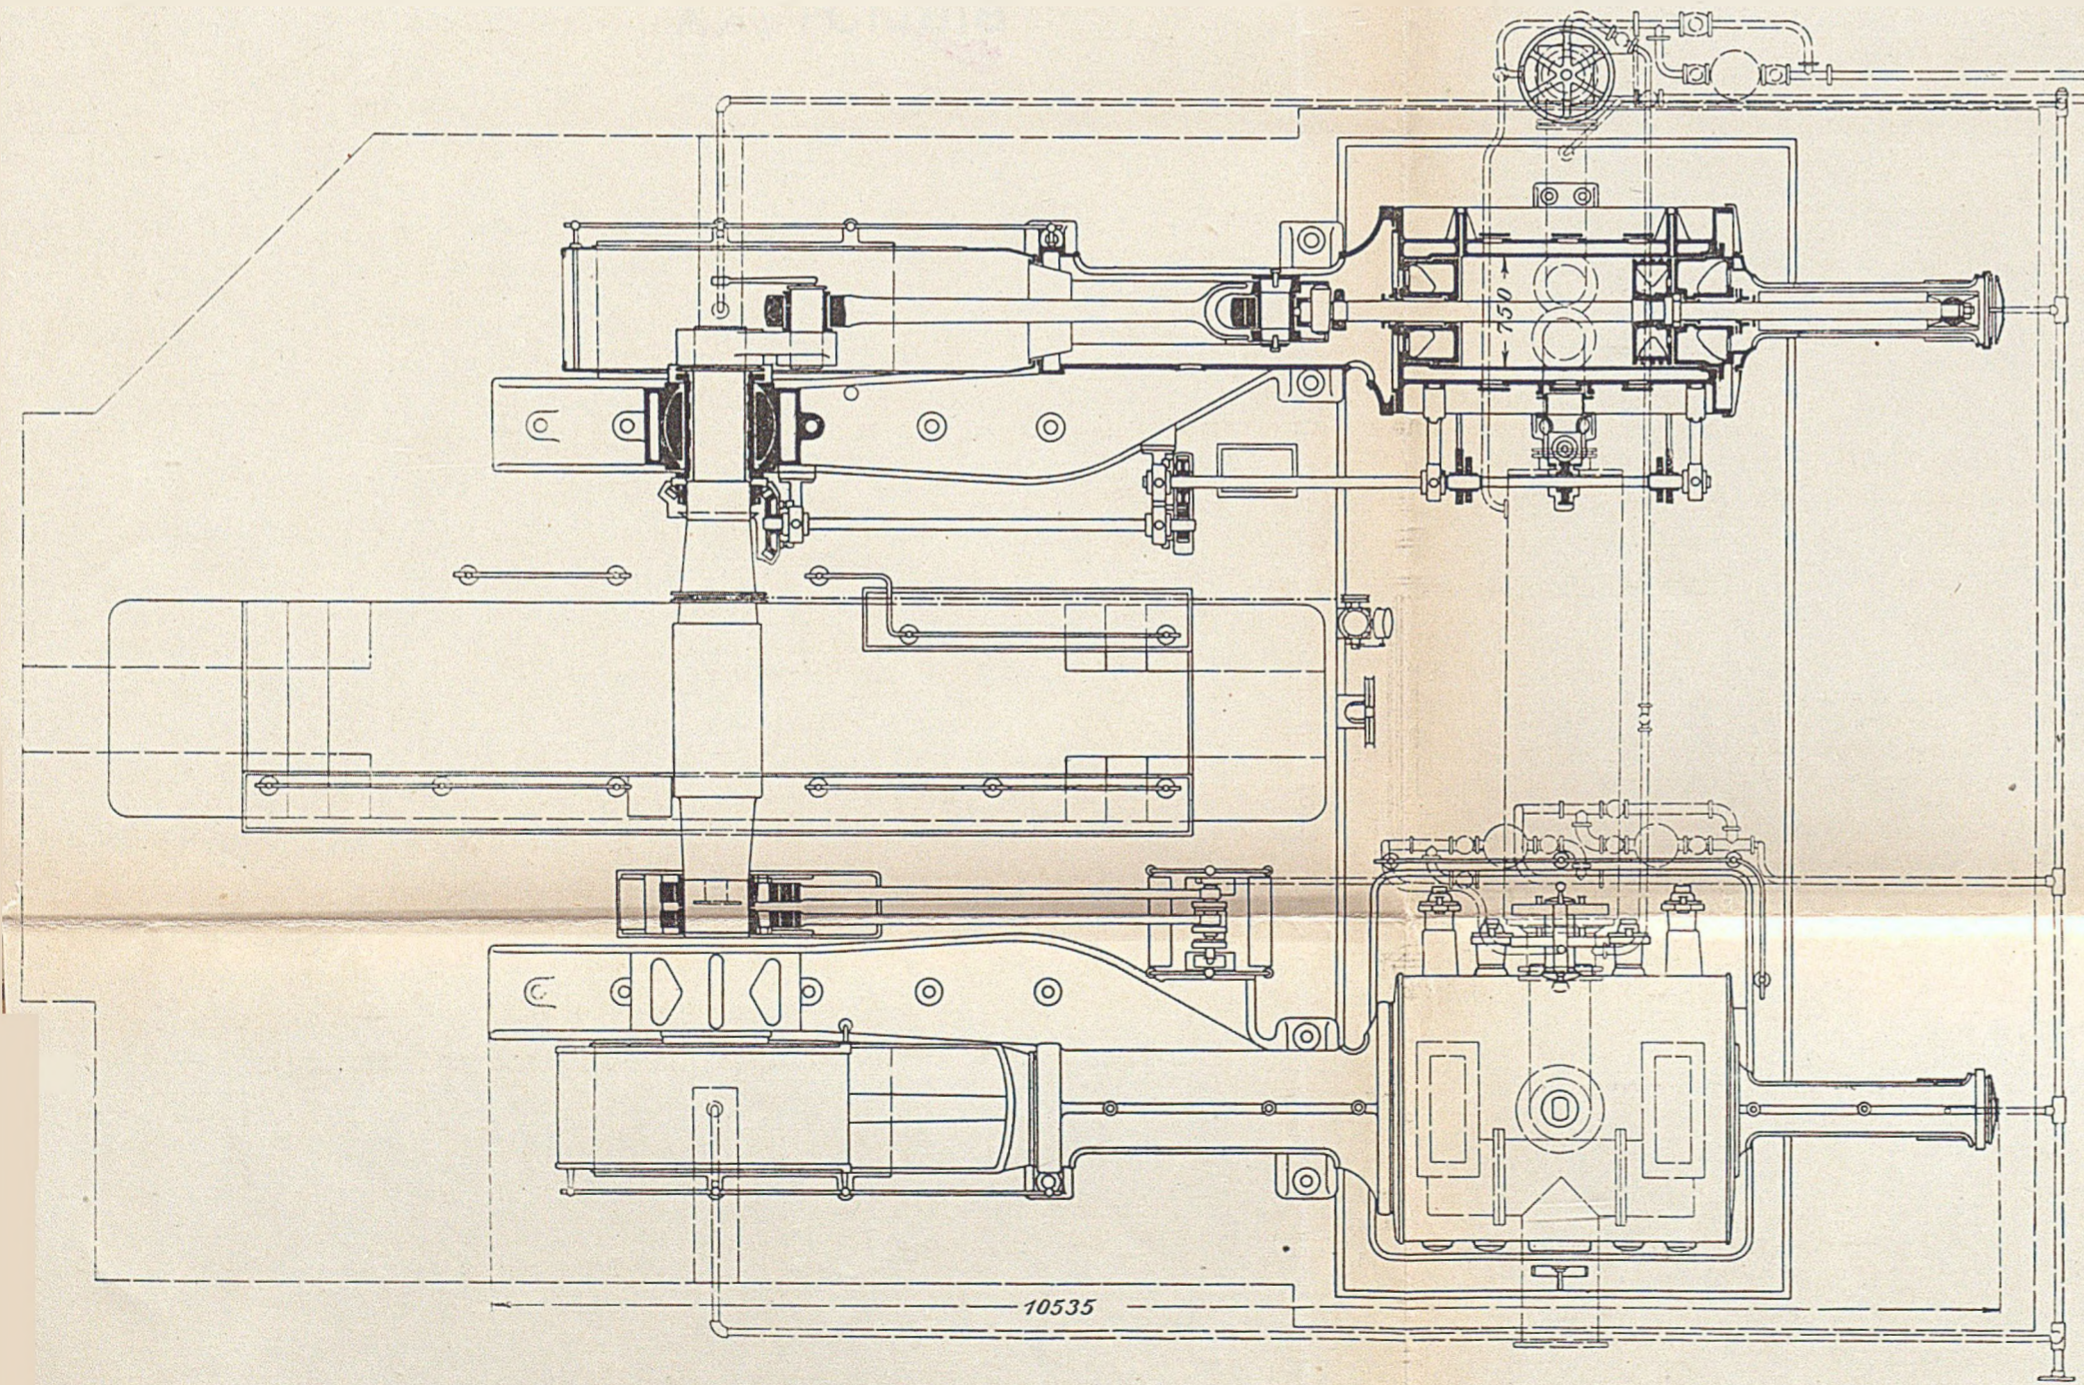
Grundriß sowie Querschnitte durch den Hochdruckzylinder, ein Lager und den Steuerexzenter des Niederdruckzylinders.
